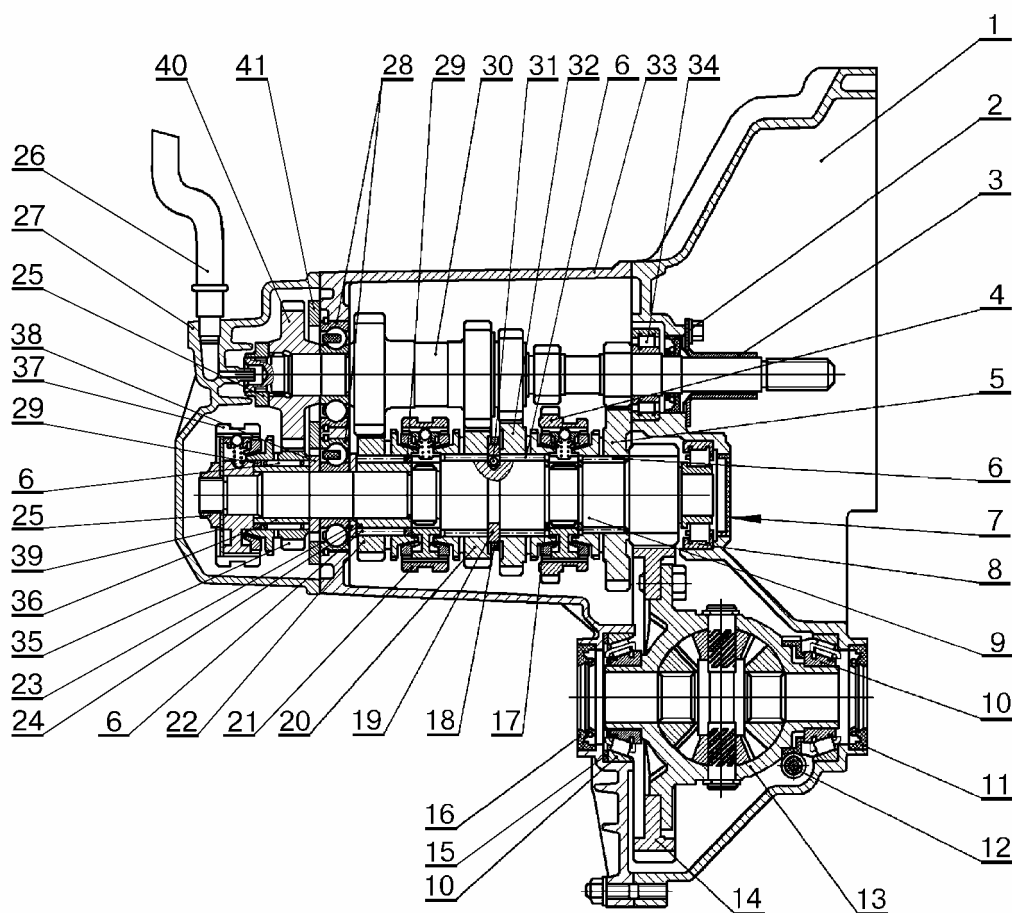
Пятиступенчатая коробка передач автомобилей семейства ВАЗ 2108/09:
